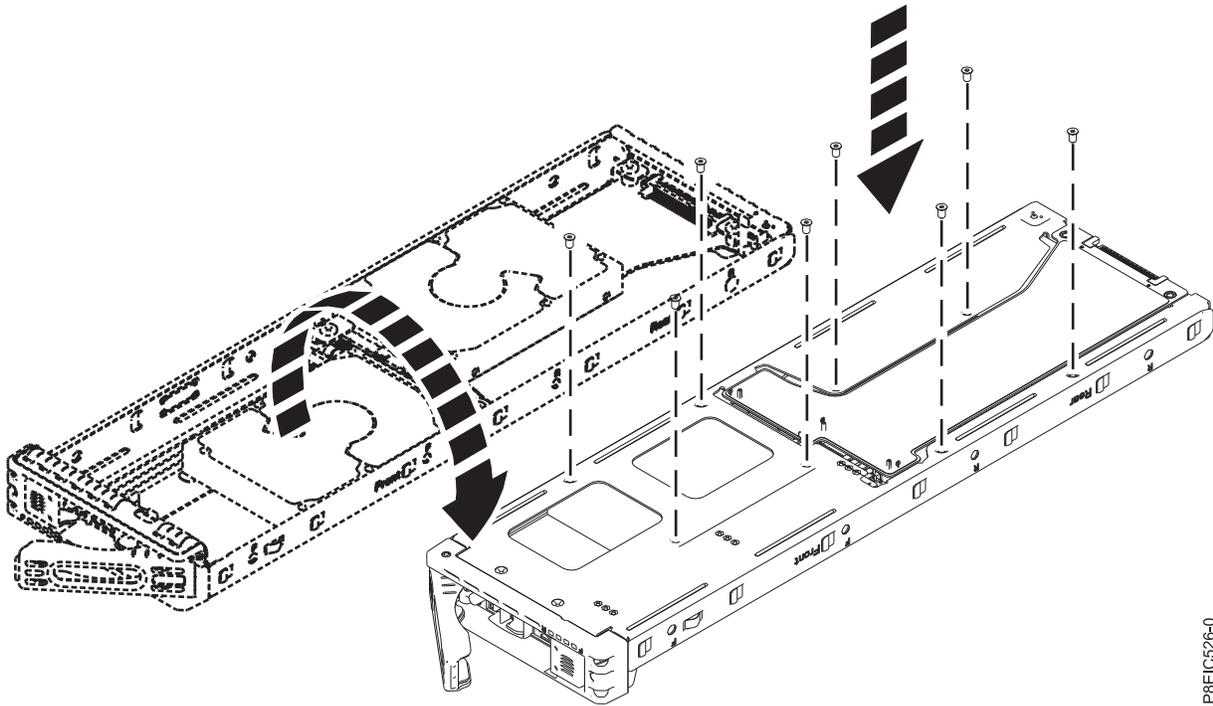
Positionen der Schrauben beim 2,5-Zoll-Laufwerk
